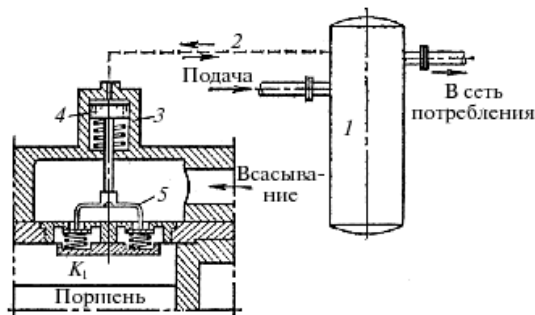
Схема регулирования подачи компрессора отжиманием пластин всасывающего клапана
